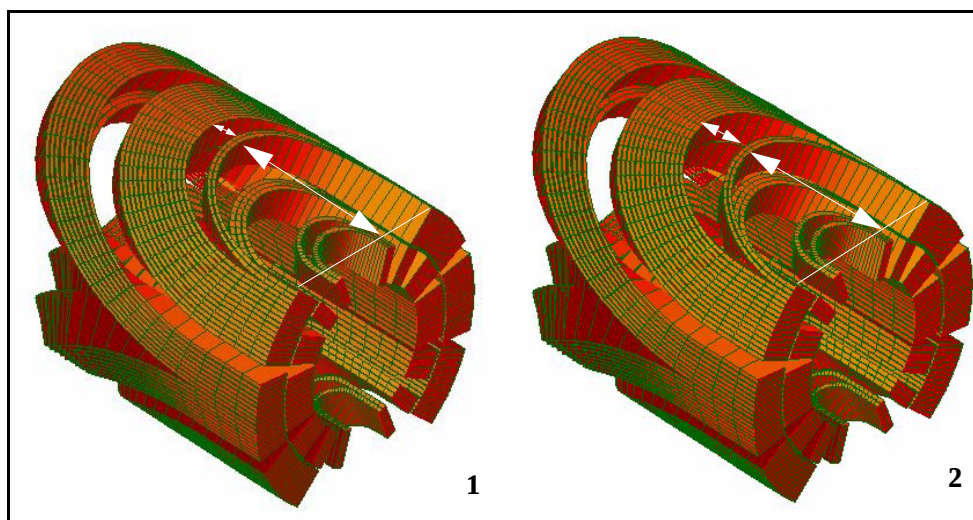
Aspetto della bobina lato non connessione elaborato in ROXIE: (1)layout attuale dei conduttori; (2)layout modificato con lo spostamento di 10 mm dei conduttori più interni dello strato superiore.
